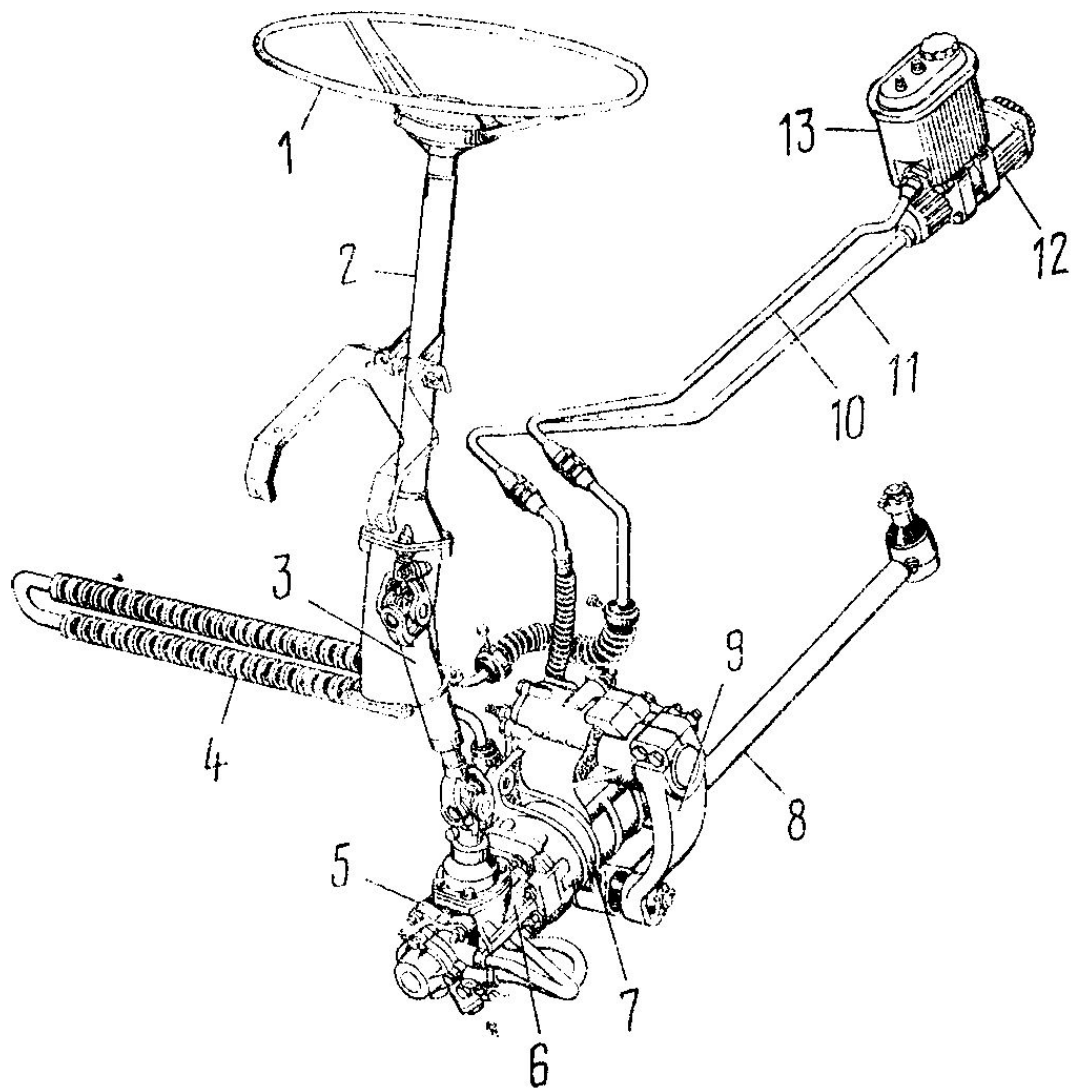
Управление рулевое: 1 - колесо рулевое; 2 - колонка; 3 - вал карданный; 4 - радиатор; 5 - клапан управления гидроусилителем; 6 - редуктор угловой; 7 - гидроусилитель с рулевым механизмом; 8 - тяга продольная; 9 - сошка; 10 - трубопровод низкого давления; 11 - трубопровод высокого давления; 12 - насос гидроусилителя руля; 13 - бачок гидросистемы
